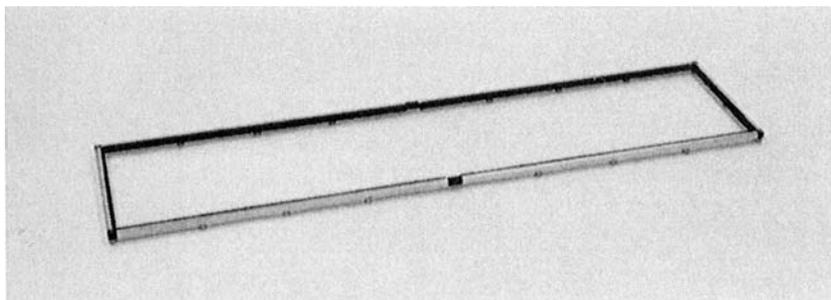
Zusammengebauter 305 mm × 1220 mm Rahmen
